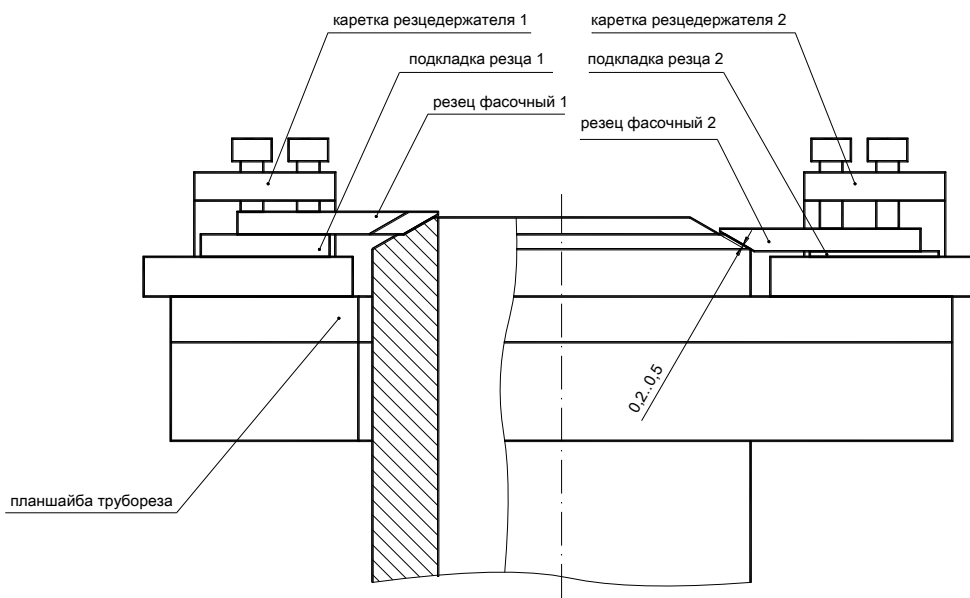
Изготовление простой наружной фаски двумя резцами отрезных суппортов
